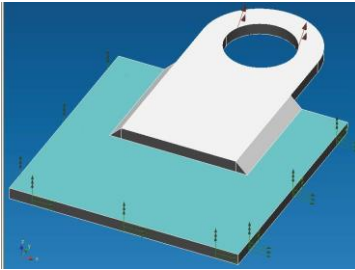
Загальний вигляд з'єднання вушка з пластиною зварним швом внапусток
